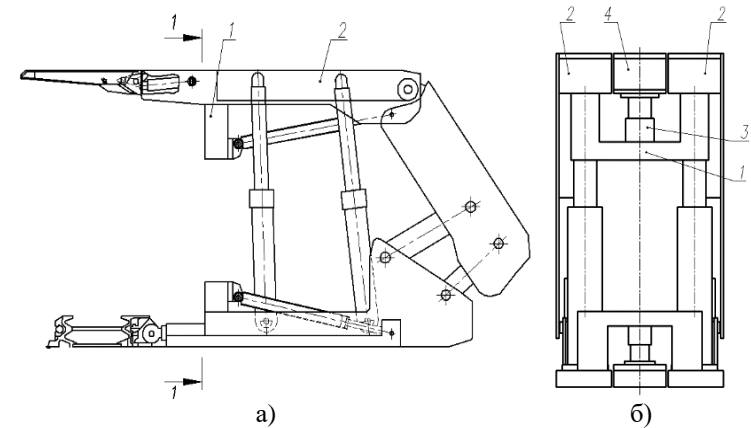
Секция механизированной крепи с опорными балками: а – секция крепи с направляющей балкой по основанию и опорной балкой по перекрытию; б – разрез 1-1; 1 – портал; 2 – перекрытие секции крепи; 3 – гидропатрон, шарнирно соединенный с опорной балкой 4
